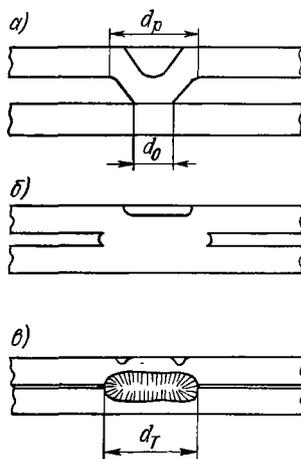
Схема формирования рельефно-сварного соединения
